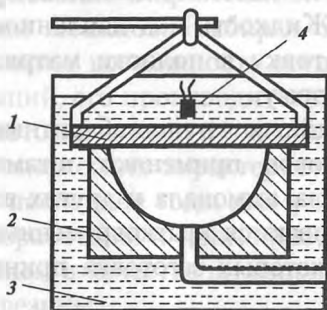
Схема штампования в воде (штамповка взрывом): 1 — заготовка; 2 — матрица; 3 — емкость с водой; 4 — заряд взрывчатого вещества
